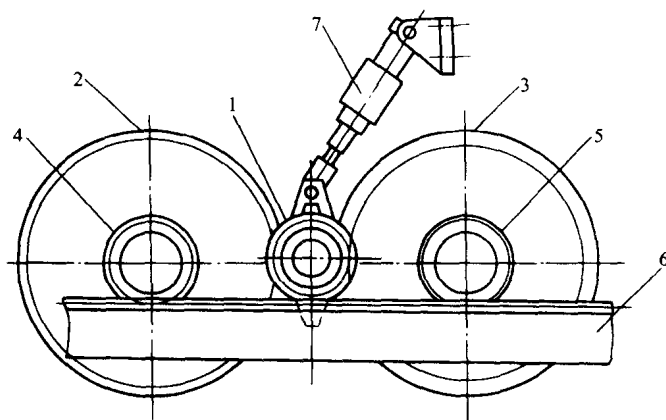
齿轮齿条啮合齿侧隙消除法结构简图
